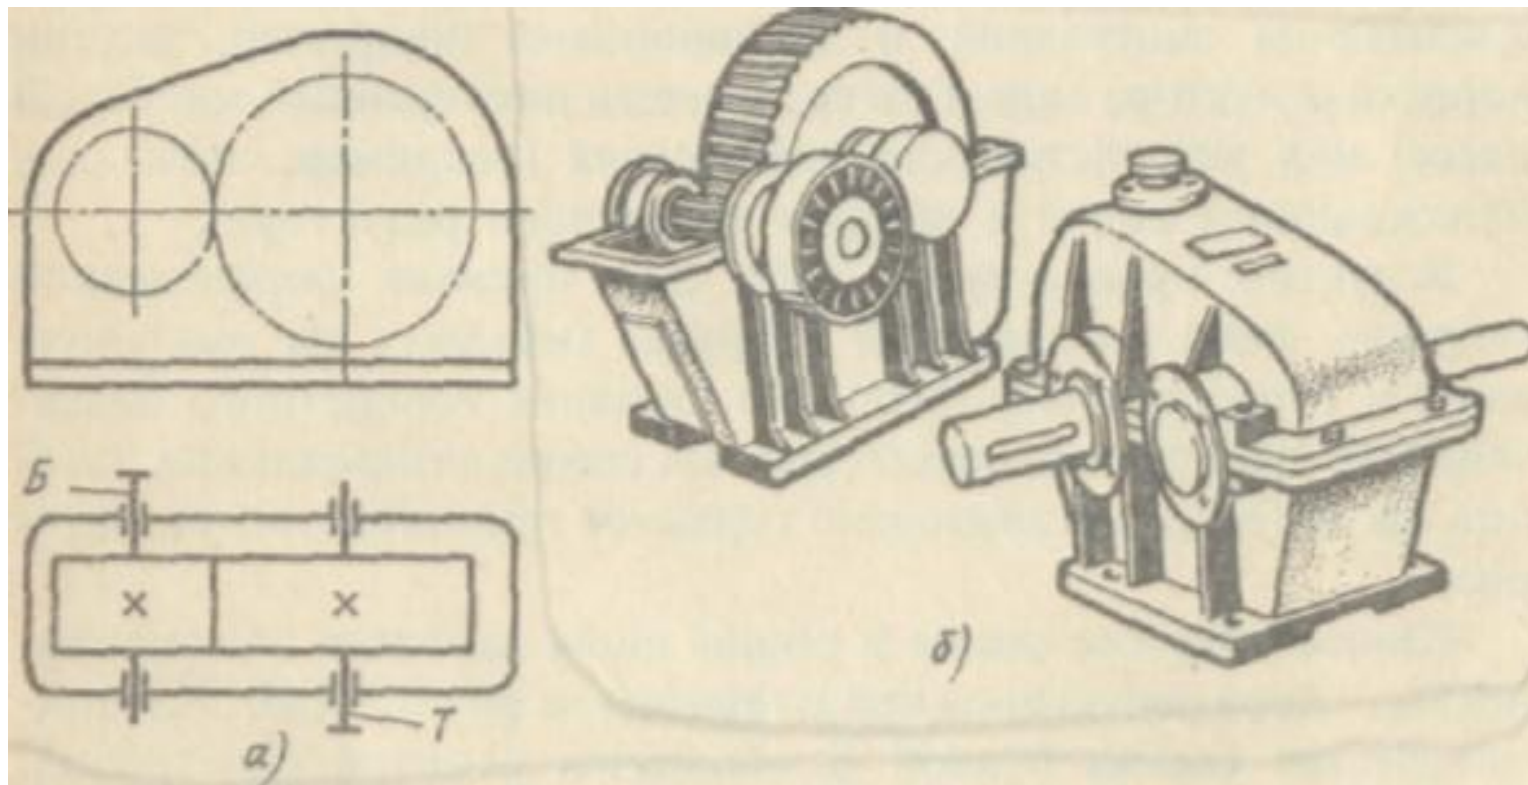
Одноступенчатый горизонтальный редуктор с цилиндрическими зубчатыми колесами:
